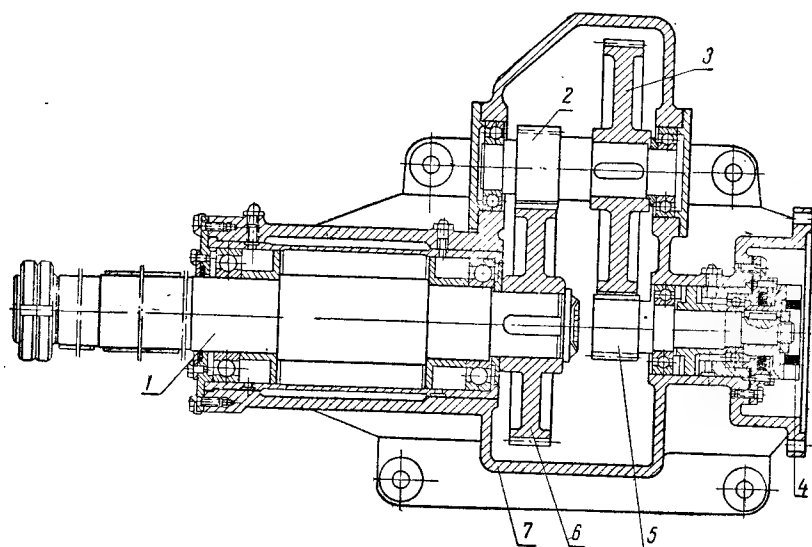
Редуктор агрегата ВЭВ-1-6:
